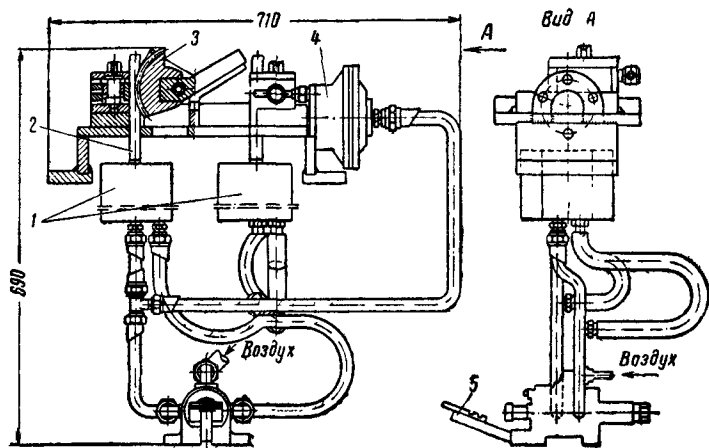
Пневматическое приспособление для развода головок якорных катушек тяговых двигателей:
